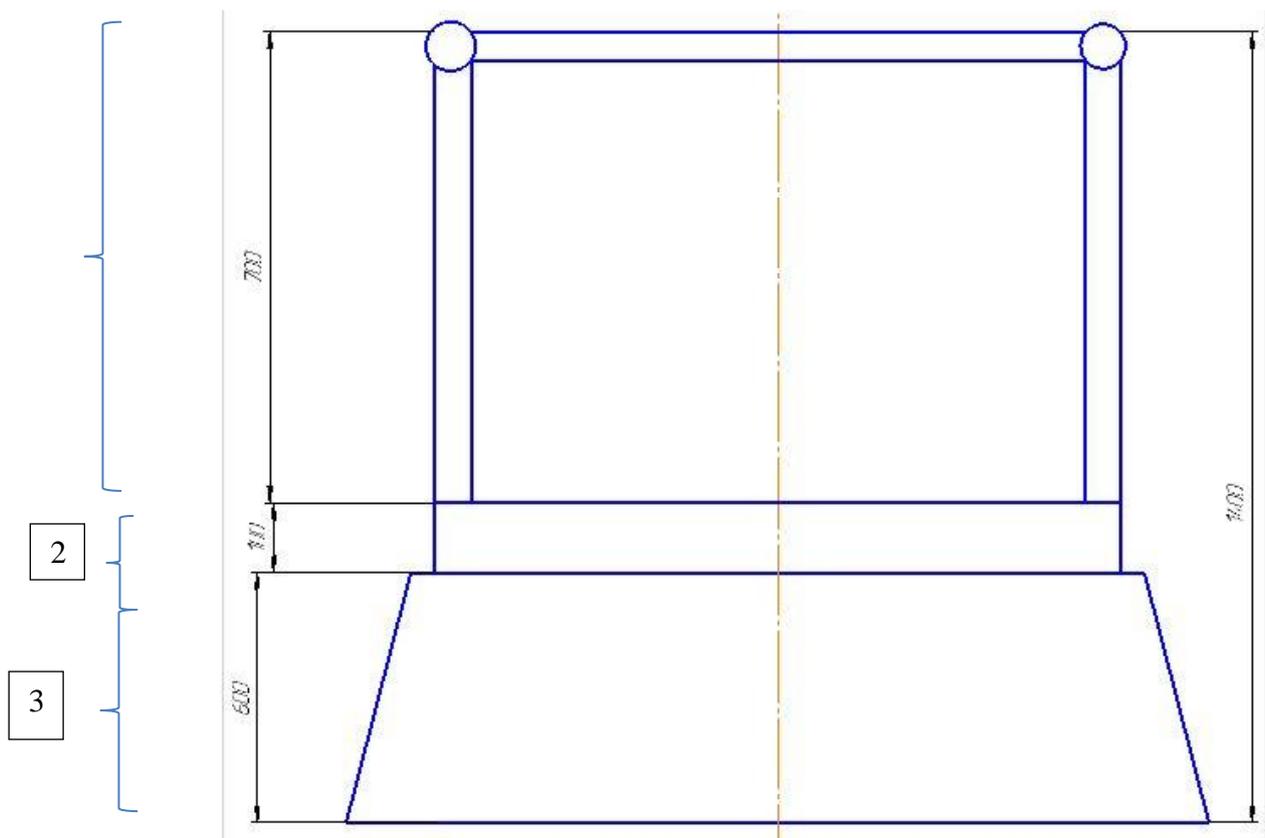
Схема мобильного станка робота (1-рама станка; 2-раздвижной стол; 3-корпус)
